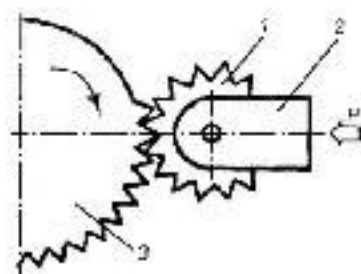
Принципиальная схема восстановления накаткой: 1 — накатный ролик; 2 — приспособление; 3 — восстанавливаемая деталь
